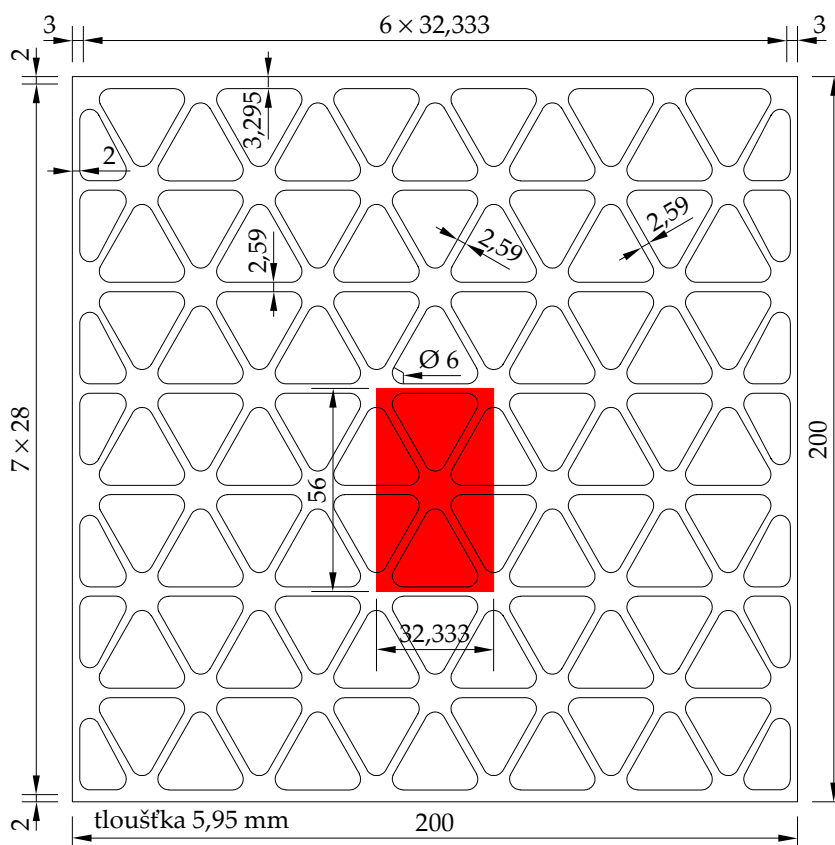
Geometrie perforované desky PWC 6-24b
